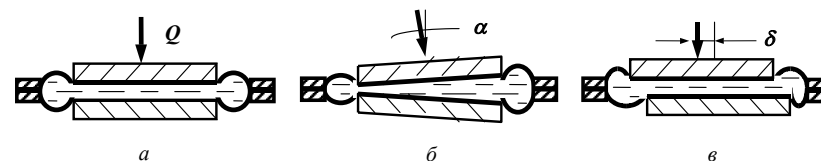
Схемы возможного приложения силовой нагрузки к гидрокапсуле.
